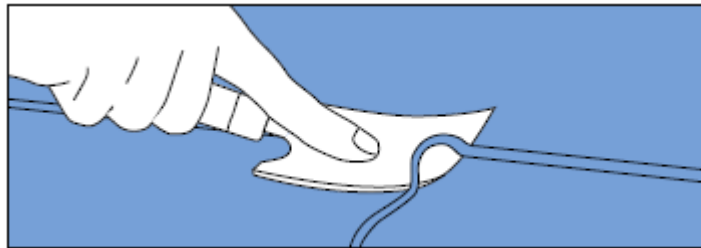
Segundo corte executado após arrefecimento do cordão de soldadura [11]
